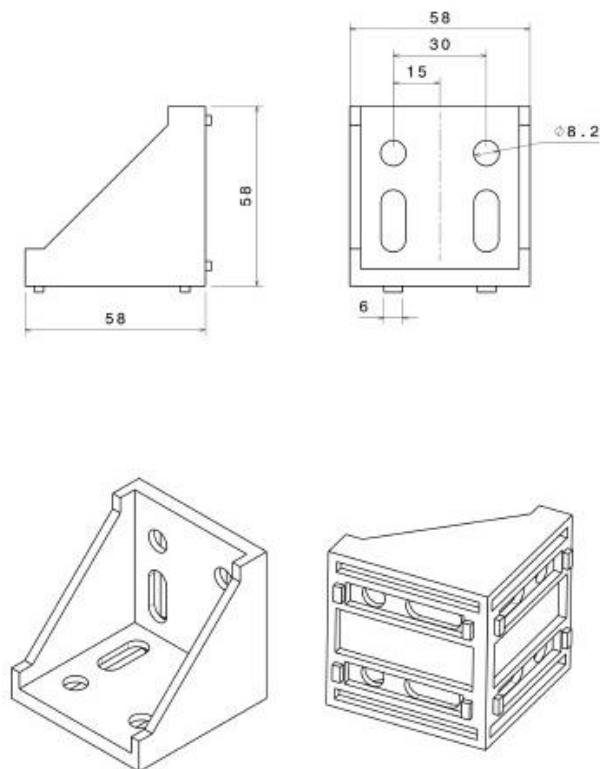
Dimensiones escuadra de fundición de aluminio para perfil de aluminio de 60x60 mm
